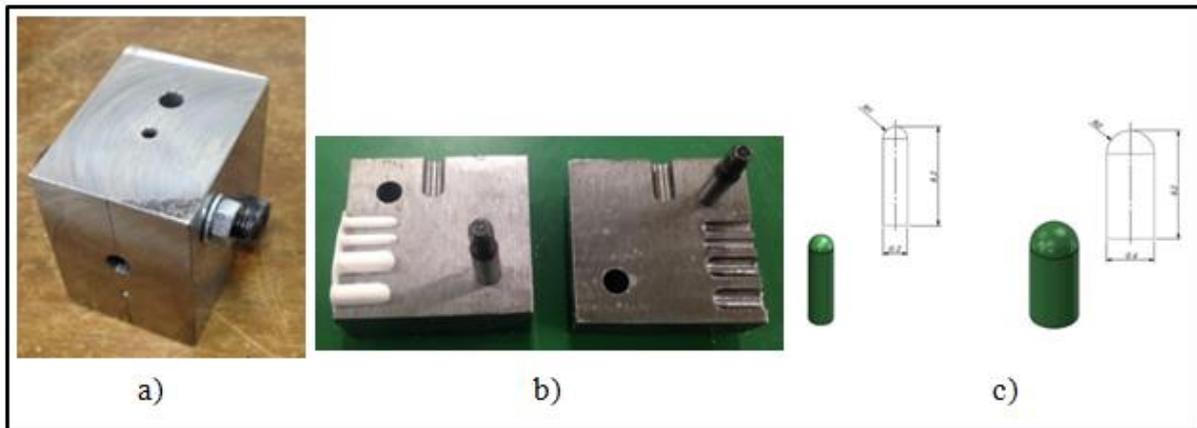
Molde bipartido de aço inoxidável para fabricação dos eixos hemisféricos: a) Molde fechado; b) Molde aberto com quatro eixos nele produzidos; c) Dimensões dos eixos.
